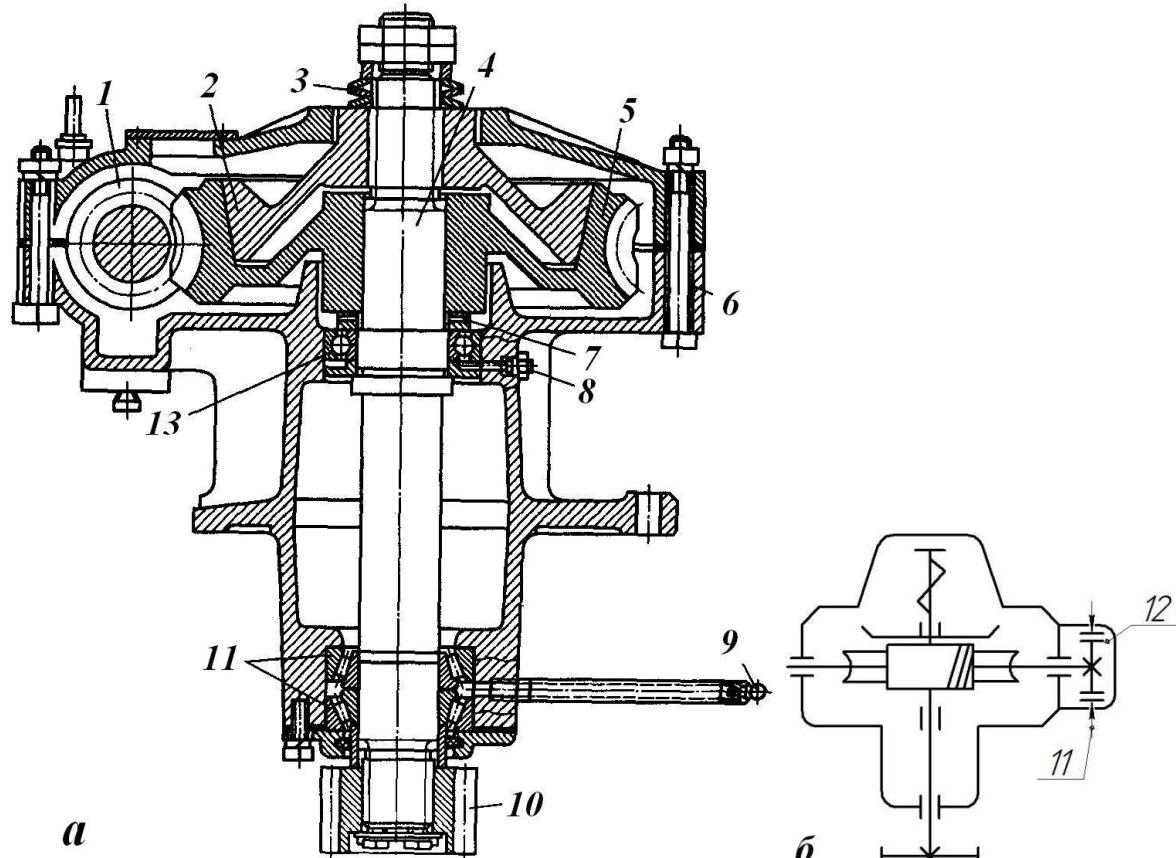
Механизм поворота крана КС-2561Е с фрикционной предохранительной конической муфтой: *а* – общий вид муфты, *б* – кинематическая схема механизма, 1 – червяк, 2 - диск, 3 – пружины, 4 – вал, 5 – червячное колесо, 6 – корпус, 7 – регулировочные шайбы, 8, 9 – пресс-масленки, 10 – шестерни, 11 – конические роликовые подшипники, 12 – ленточный тормоз, 13 – шариковый подшипник
